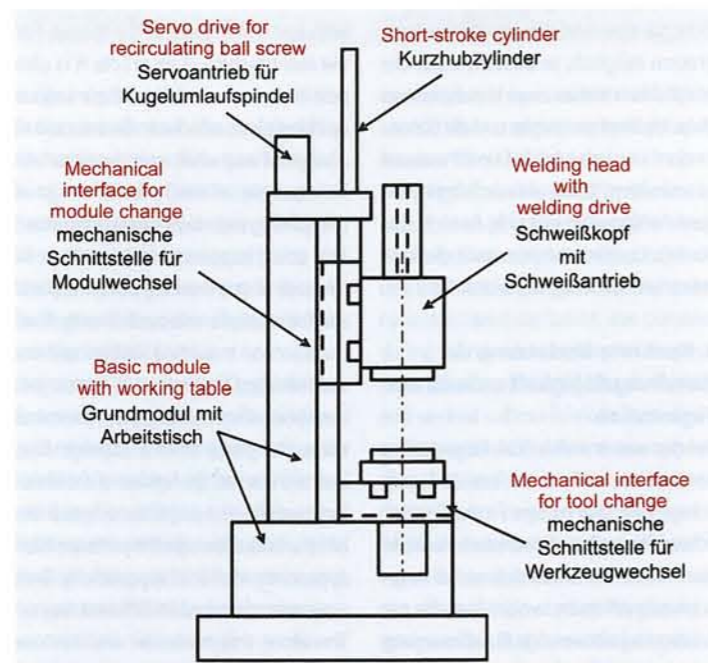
Skizze der modular aufgebauten Schweißmaschine
